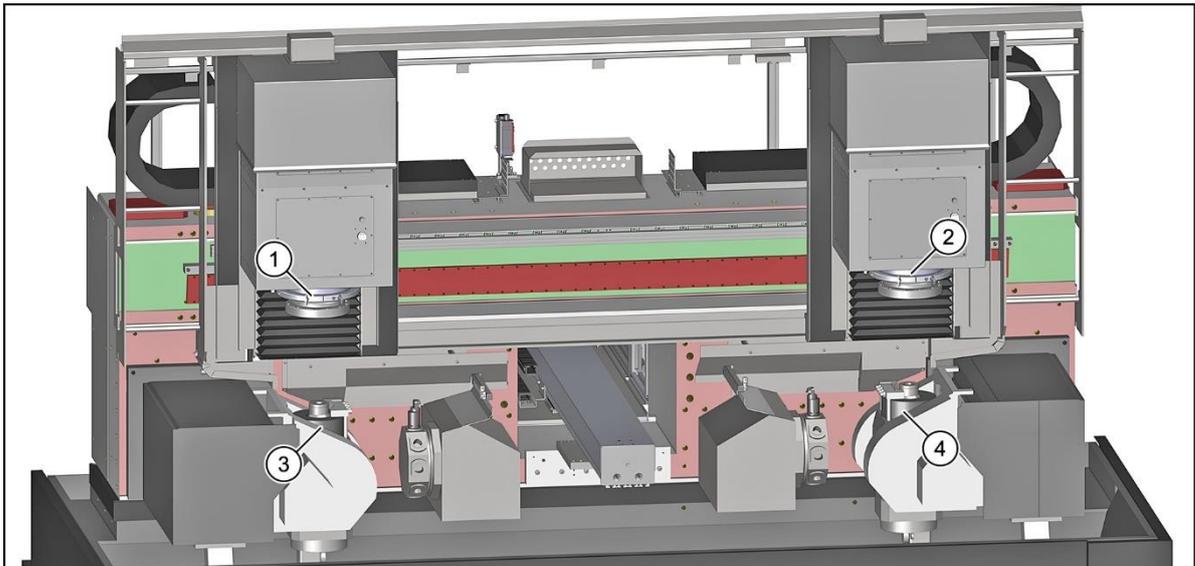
Übersicht Schwingungssensoren Wälzschälmaschine - SynchroForm
